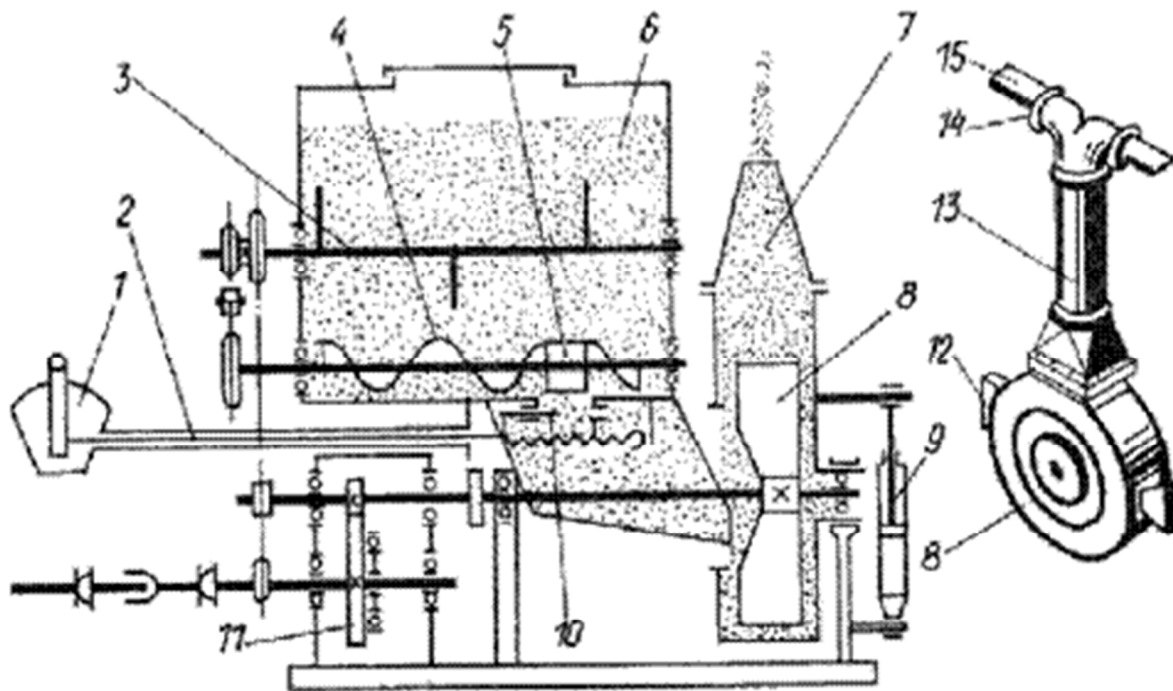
Опыливатель широкозахватный универсальный ОШУ-50:
